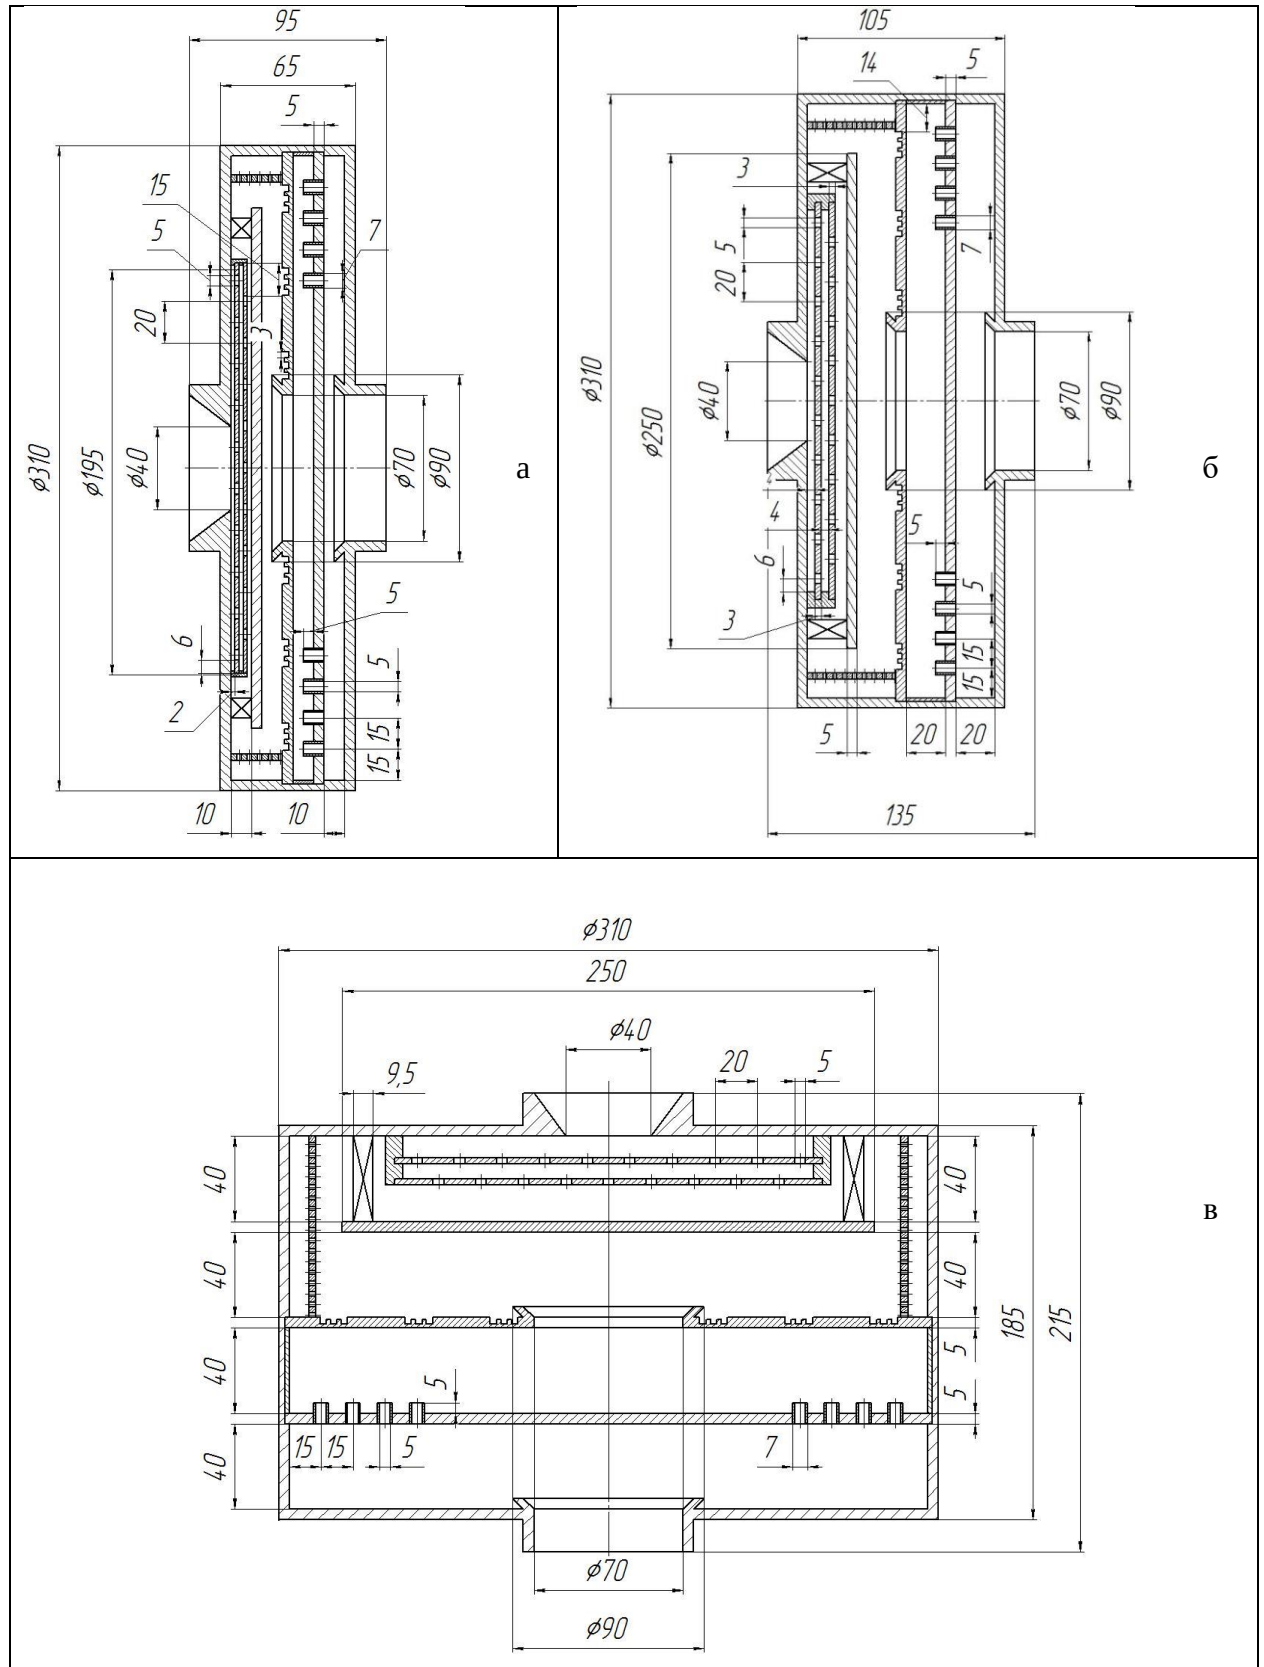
Робоча геометрія сепаратора паливного газу. Конструктивна схема 1. Розмір ступеня попередньої очистки:
